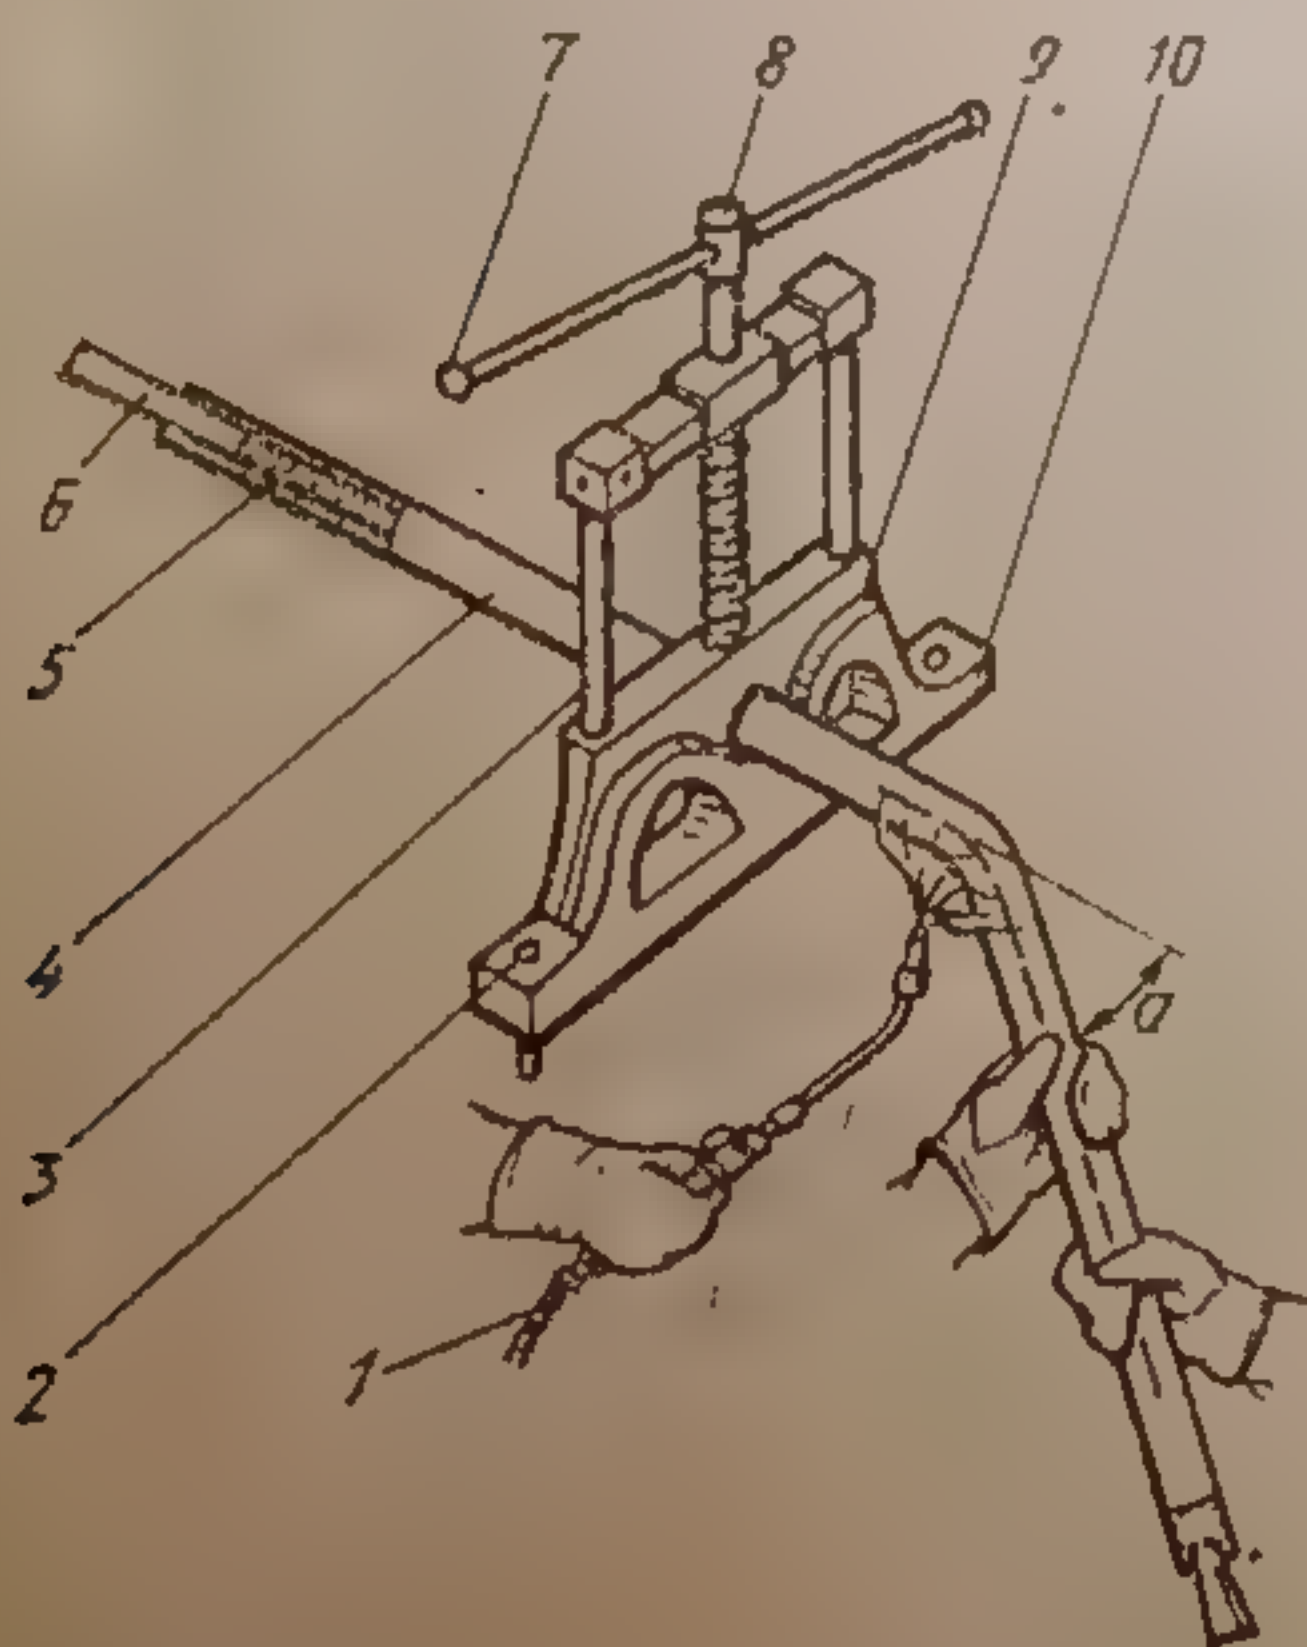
Гибка трубы в горячем состоянии на прижиме: 1 — горелка; 2 — болт крепления прижима; 3 — колонна; 4 — изгибаемая труба; 5 — песок; 6 — пробка; 7 — рычаг; 8 — прижимной винт; 9 — призма; 10 — корпус
